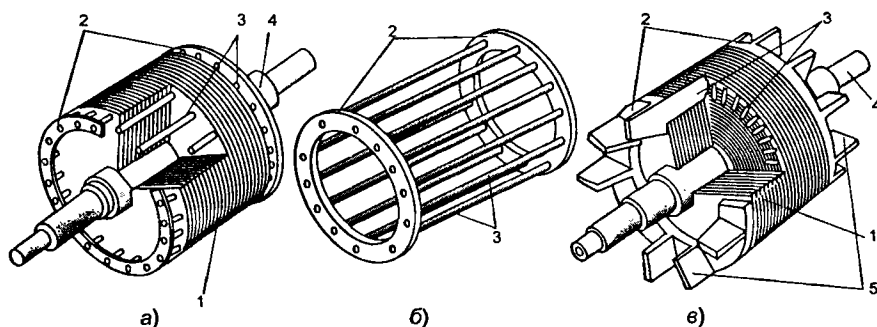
Короткозамкнутый ротор асинхронного электродвигателя: а — с вставленными в пазы стержнями; б — «беличья клетка»; в — с обмоткой, выполненной заливкой алюминиевого сплава; 1 — сердечник ротора; 2 — короткозамыкающие кольца обмотки; 3 — стержни обмотки; 4 — вал; 5 — вентиляционные лопасти
